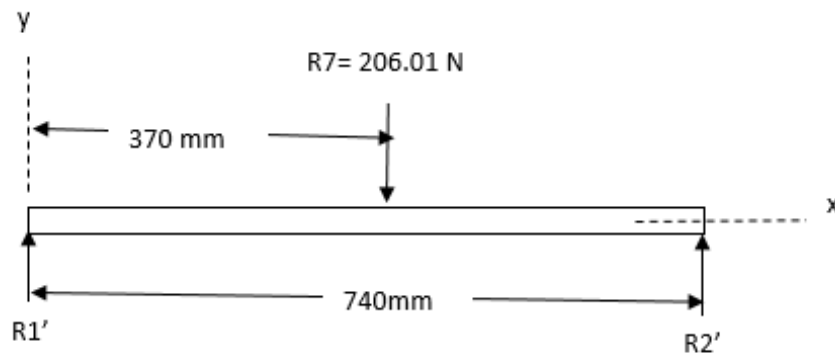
DLC de la viga longitudinal de la zona de trabajo.
